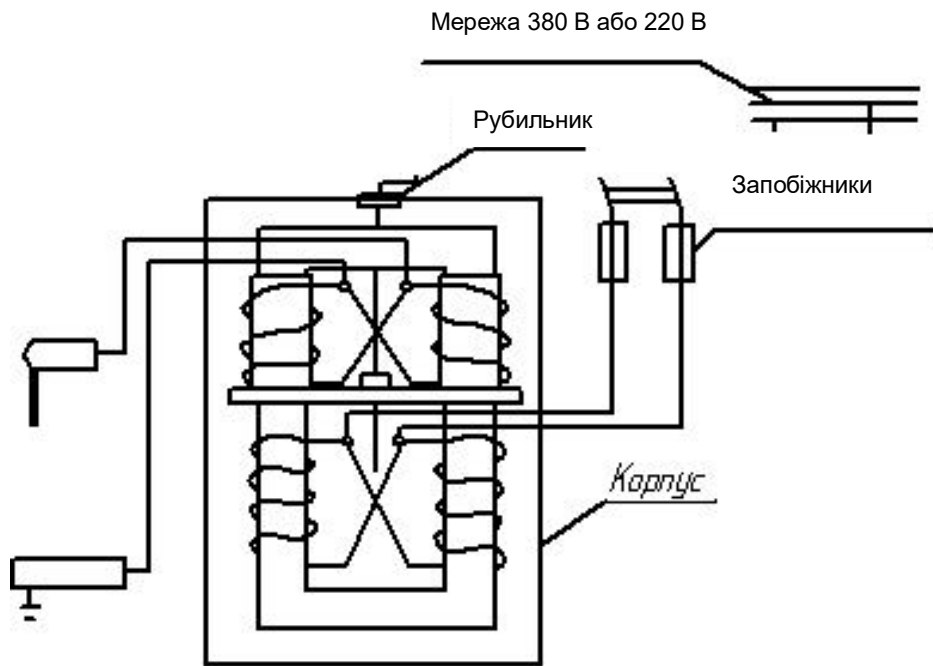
Принципова електрична схема зварювального трансформатора з рухомими котушками вторинної обмотки.
